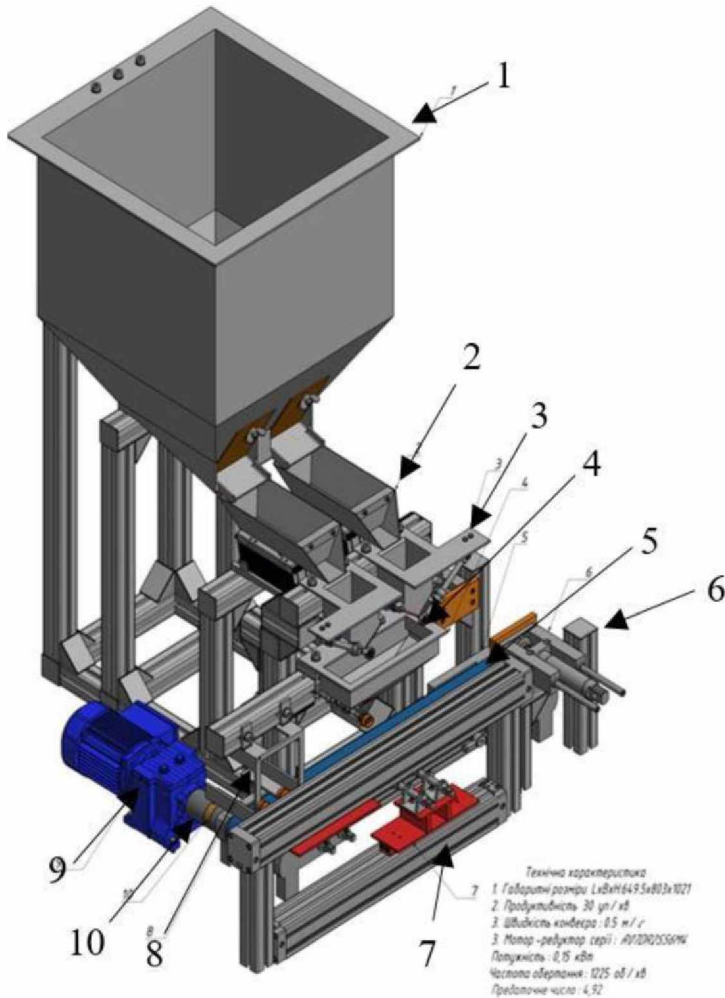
Загальний вид машини: 1 – бункер; 2 – віброструшувач NVB07; 3 – мірна ємність; 4 – дозувальна ємність; 5 – стрічковий конвеєр; 6 – лінія затискання пачки; 7 – модуль захоплення та транспортування упаковки; 8 – магазин для упаковки; 9 – мотор-редуктор; 10 – муфта
